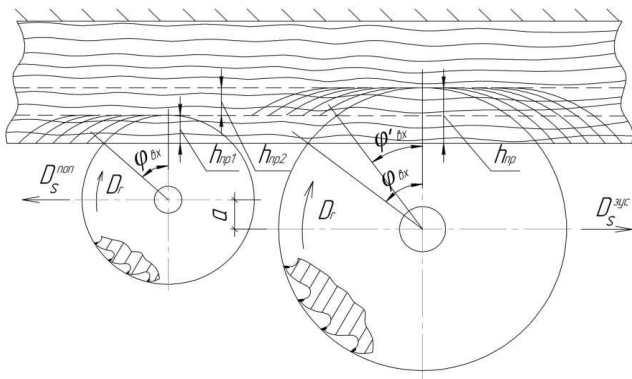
Схема різання підрізною і основною пилками під час глухого пиляння із зустрічною та попутною подачею
